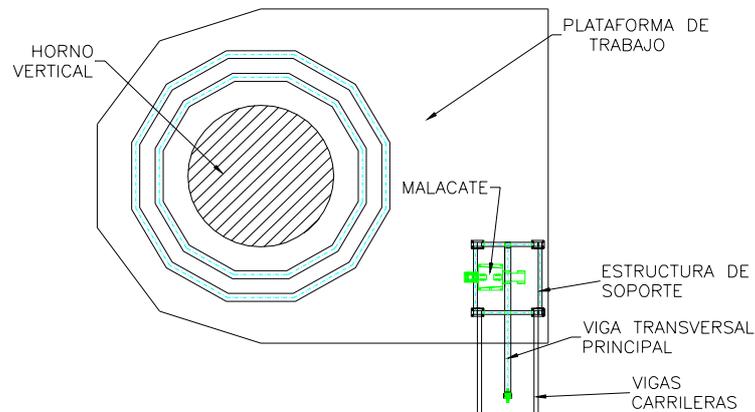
VISTA DE PLANTA DE GRÚA ESTÁTICA.
